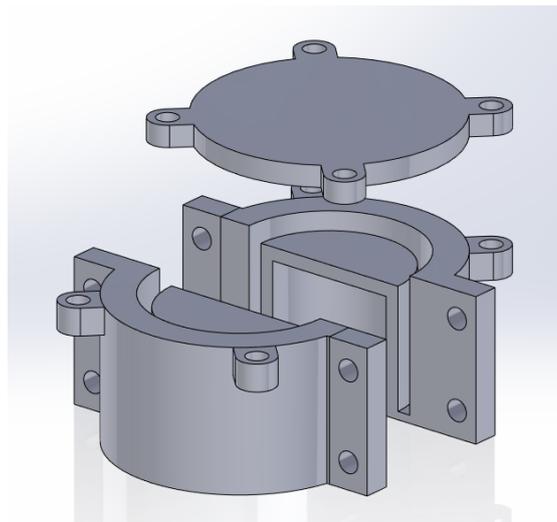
Molde de injeção da peça a inserir no tubo principal
